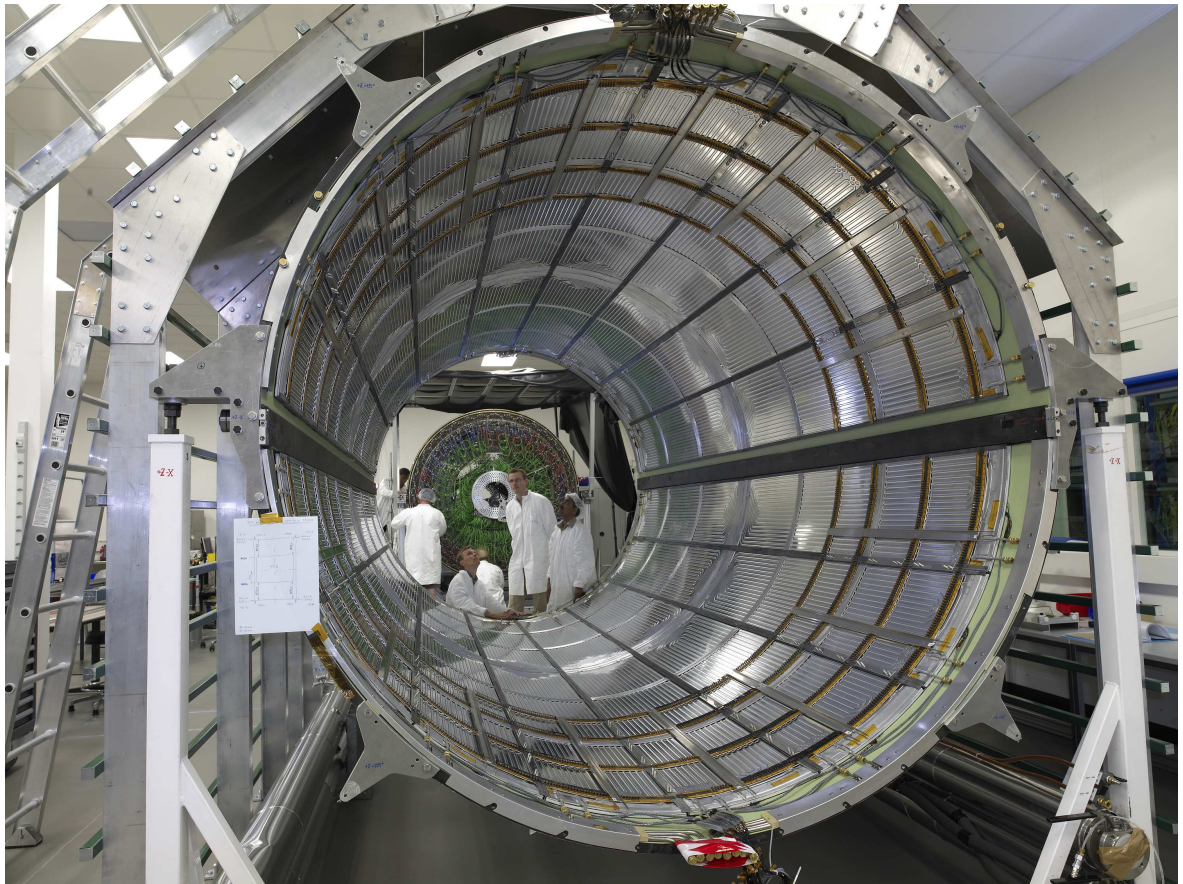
L'écran thermique placé au sein du tube support du trajectographe et ses 32 panneaux régulateurs.
